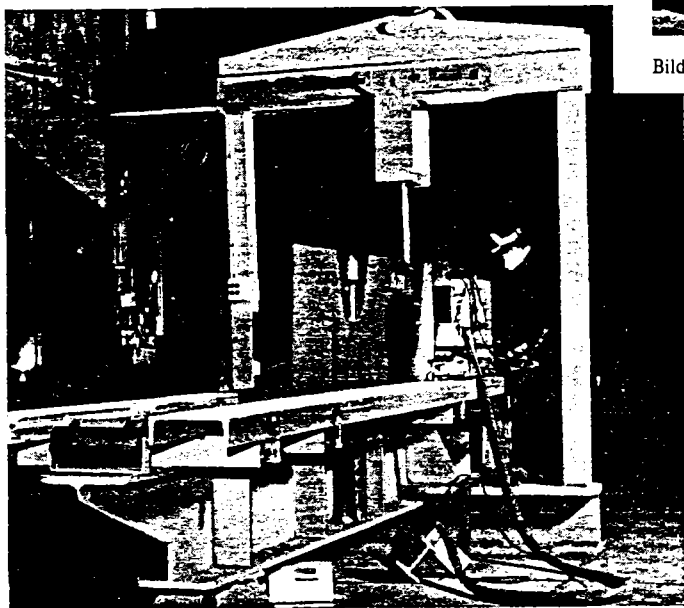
Schweißstation mit Schutzgas-Schweißautomat
